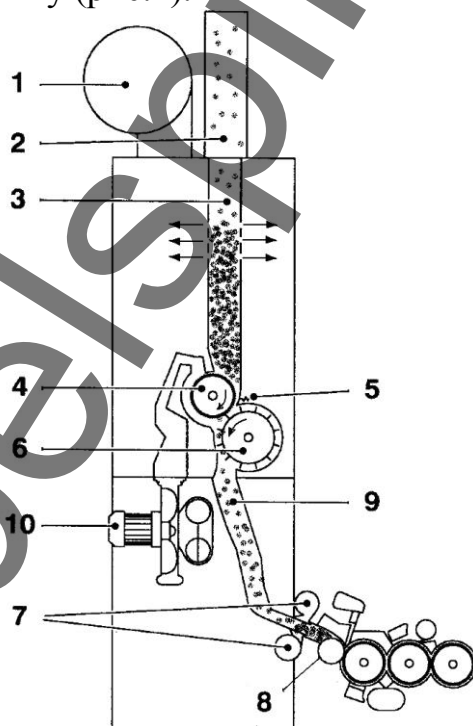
Конструкция бесхолстового питателя DIRECTFEED ф. Trutzschler: 1 – пылеотсасывающий патрубок; 2 – загрузочная шахта верхней камеры; 3 – верхняя камера; 4 – питающий валик; 5 – питающий столлик нижней камеры; 6 – разрыхлительный барабан; 7 – каналы для отвода воздуха; 8 – выпускной цилиндр бункера; 9 – нижняя камера; 10 – вентилятор
